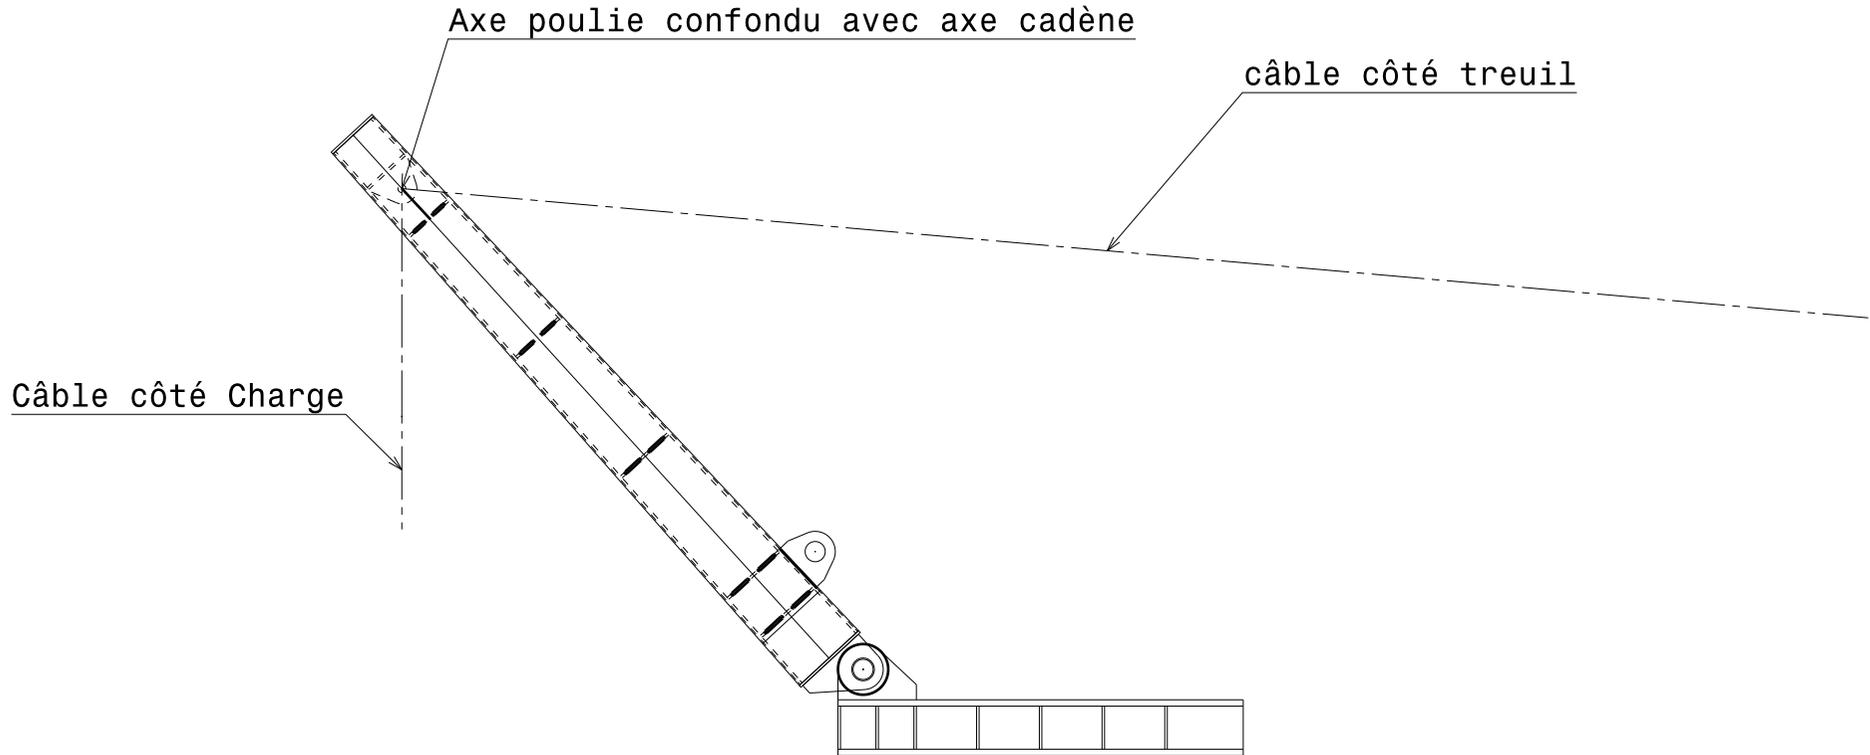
DETAIL ASSEMBLAGE CARLINGUE/CAISSON
